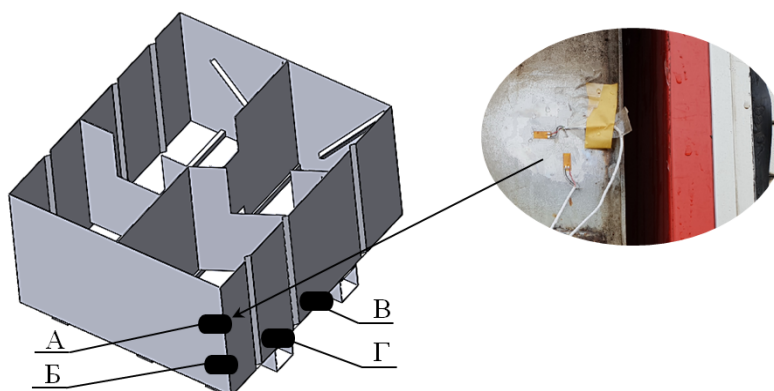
Схема установки тензорезистивных датчиков на наружной поверхности стенок цистерны пожарного автомобиля: область А, Б – угловое сварное соединение передней и боковой стенки; область В, Г – угловое сварное соединение передней стенки и дна
